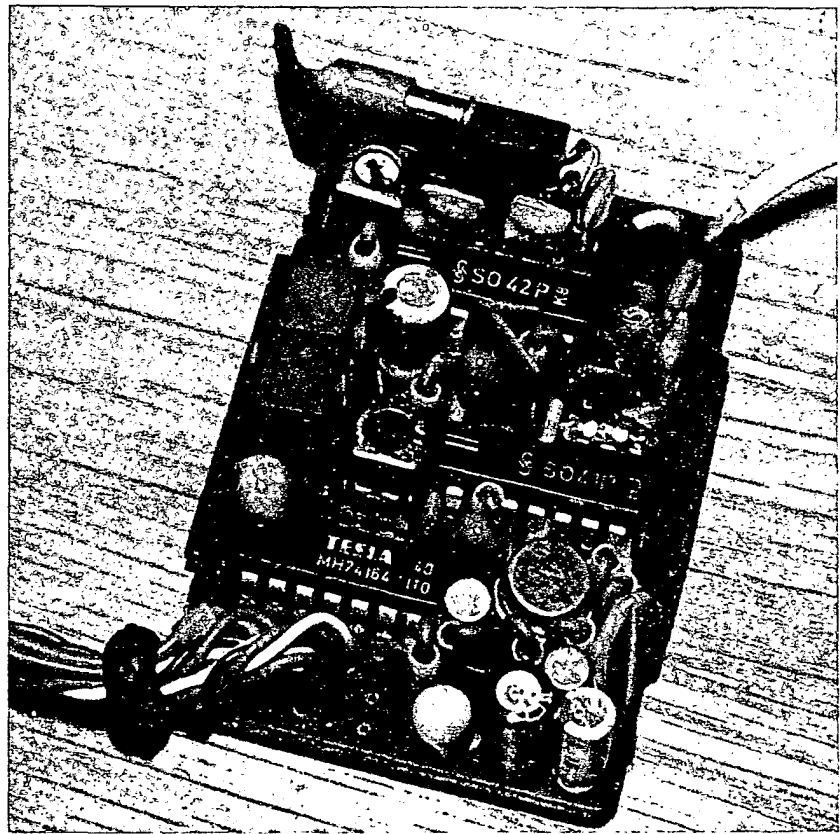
Deska s plošnými spoji P63 a rozmístění součástek
